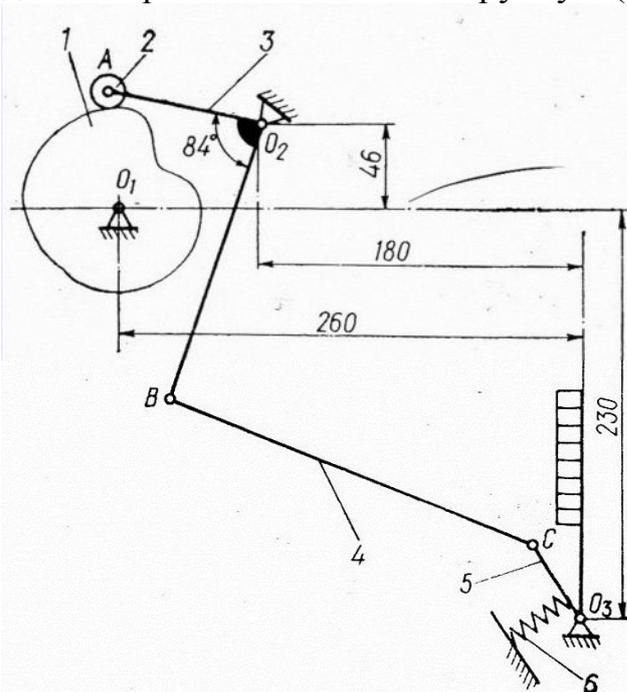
Кинематическая схема исполнительного механизма укладчика.
